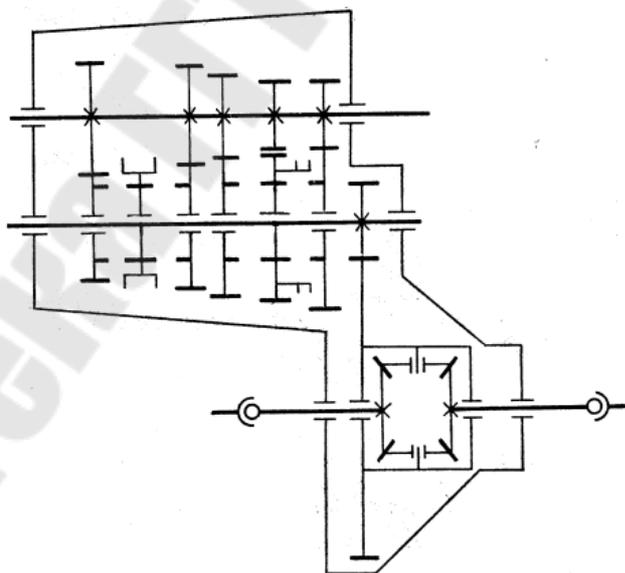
Кинематическая схема пятиступенчатой двухвальной коробки передач
